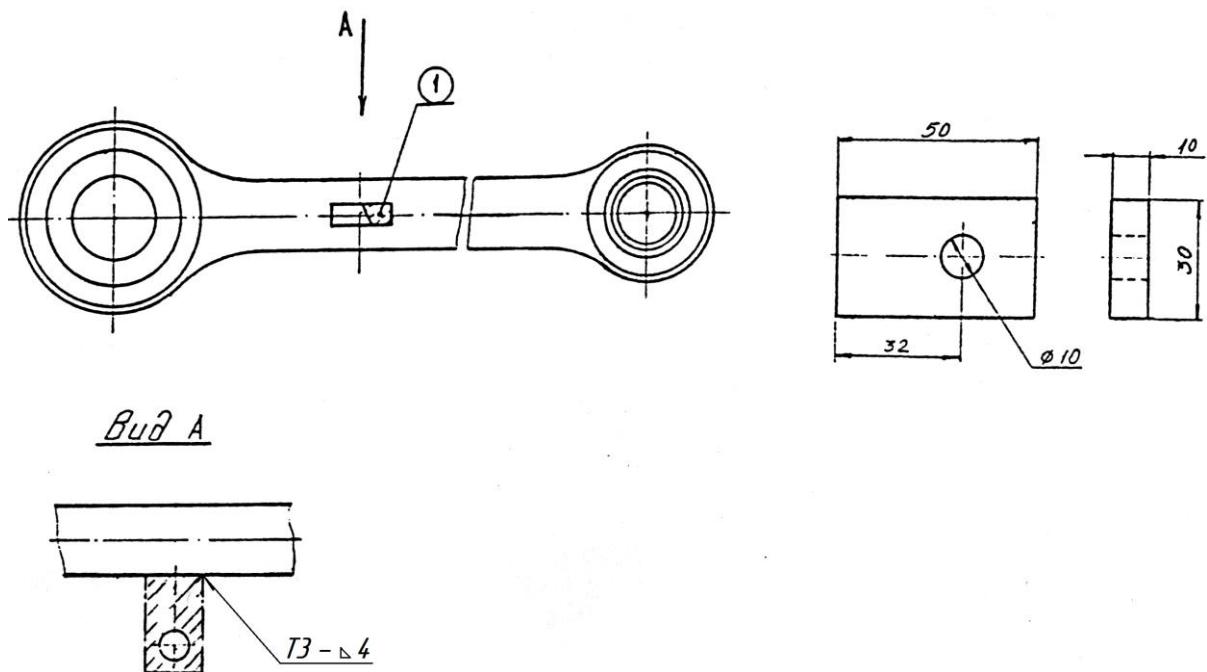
Дефекты подвески башмака, ремонтируемые сваркой или наплавкой
